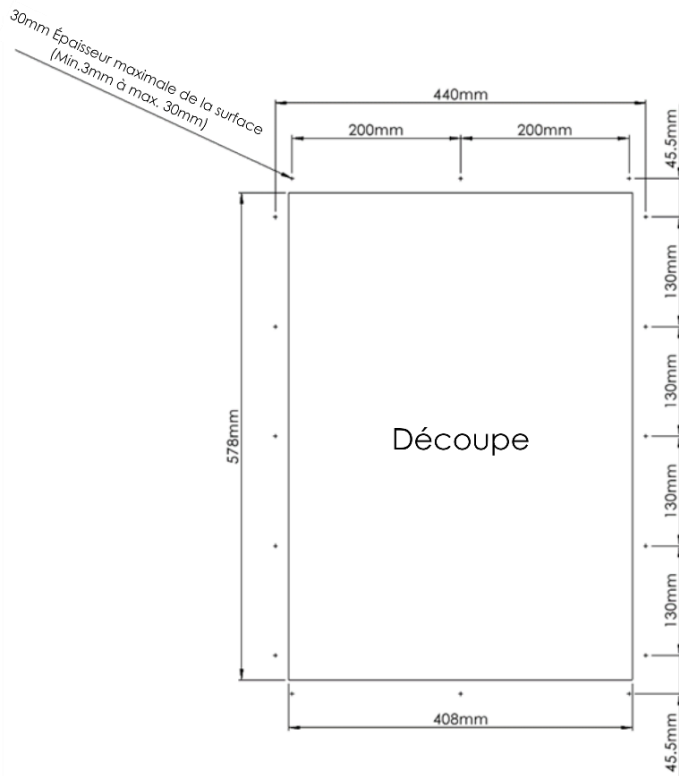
Découpe pour cadre de montage MS-MKT-GN1/1 E assemblé bord à bord
